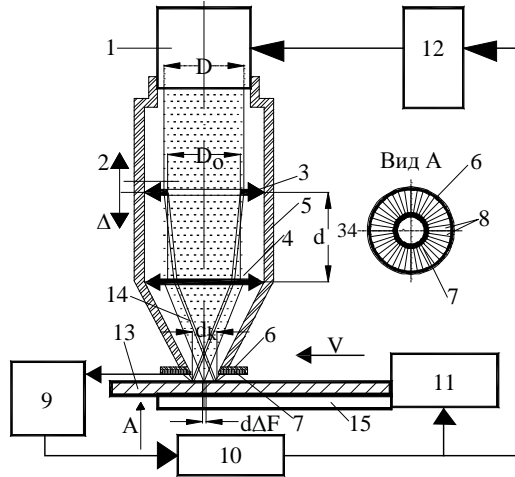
Устройство для облучения поверхности заготовки со стабилизацией уровня поглощенной энергии. (1 – лазер; 2 – луч лазера; 3 – линза с центральным отверстием; 4 – линза преобразующая; 5 – корпус; 6 – корпус датчика мощности отраженных лучей; 7 – фотодатчик с секторами; 8, 9 – измеритель; 10 – процессор; 11 – привод стола; 12 – блок питания лазера; 13 – заготовка; 14 – каустика центральной части луча); 15 – стол устройства.
